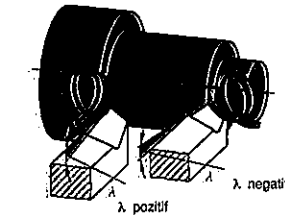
Torna kalemi (kesici kama) üzerindeki kesici ağızlar
